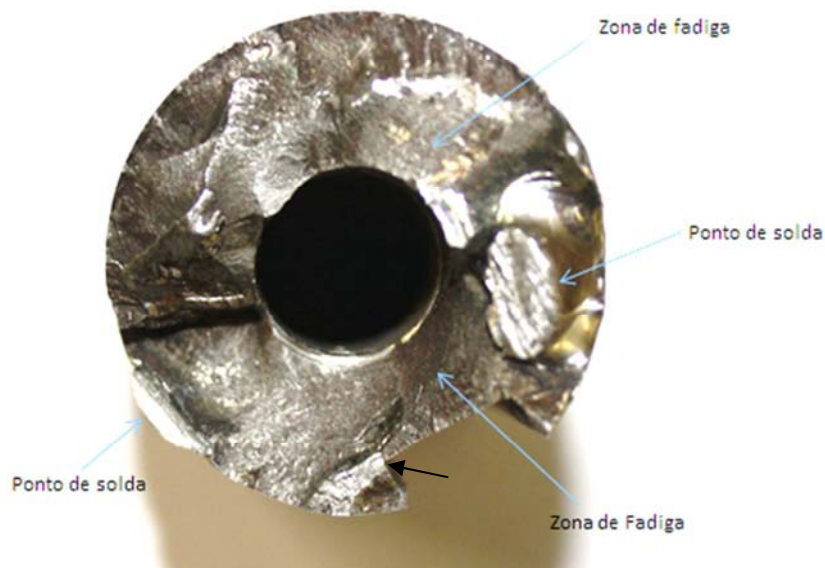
Superfície de fratura do eixo. Apresenta as marcas de solda e zona de fadiga.
